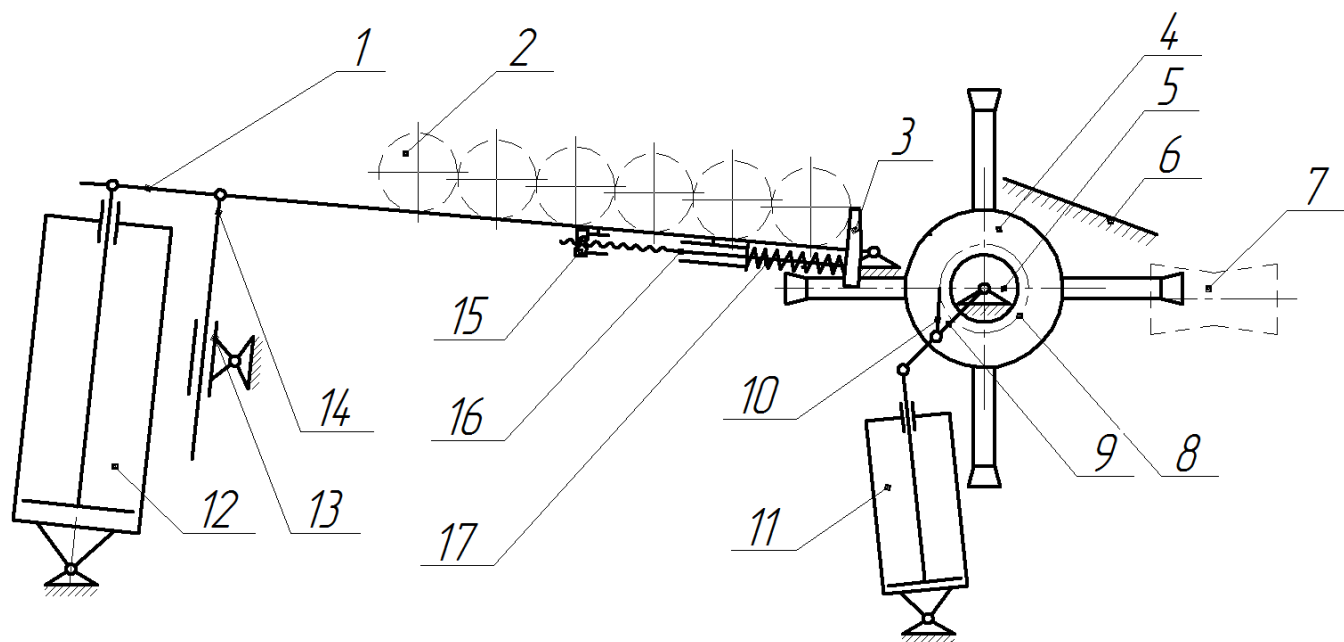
Принципиальная схема машины поштучной подачи заготовок (1 – стеллаж; 2 – заготовка; 3 – ограничитель; 4- диск; 5 – вал; 6 – склиз; 7 – рольганг; 8 – храповое колесо; 9 – рычаг; 10 – собачка; 11 – пневмоцилиндр механизма подачи; 12 – пневмоцилиндр механизма подъема; 13 – направляющая втулка; 14 – направляющая; 15 – гайка; 16 – тяга с резьбой; 17 – пружина)
